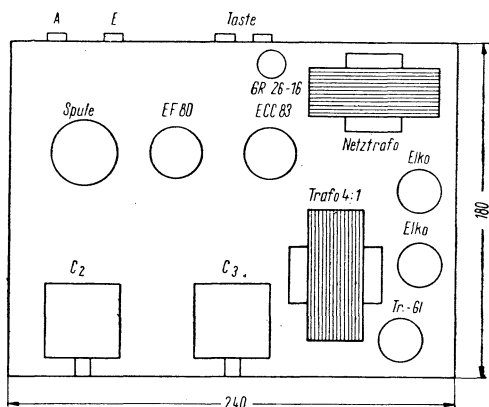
Aufbauschema der Frontplatte und des Chassis für den O-V-2 mit Tongenerator
